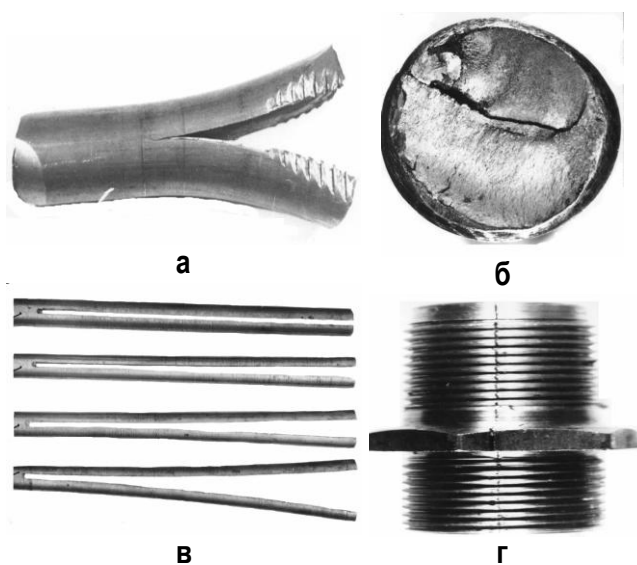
Дефекты изделий, изготовленных из калиброванного металла:
